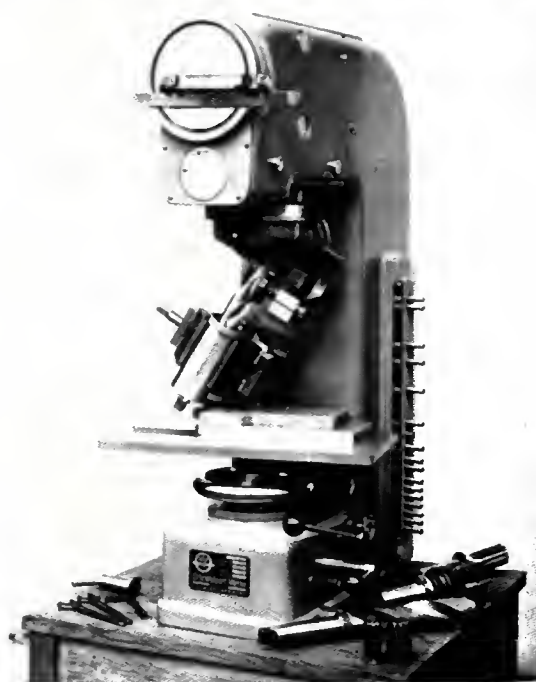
Machine pour essais de dureté Rockwell (Wolpert — Testwell)
